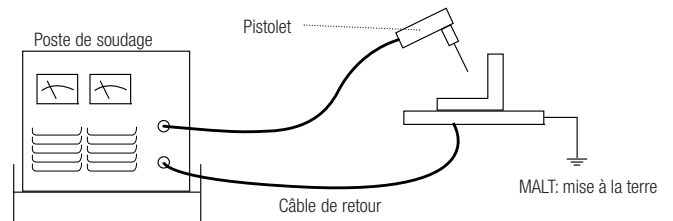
Câble de retour et mise à la terre pour le soudage à l'arc
